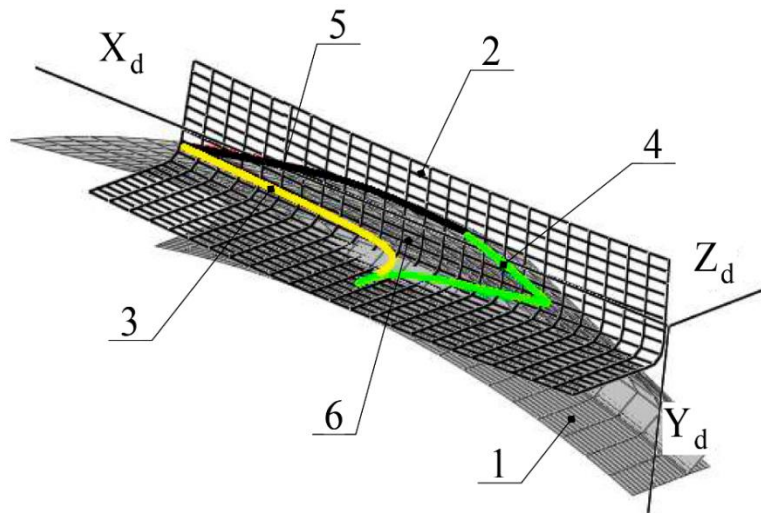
Пляма контакту зуба фрези та оброблюваної поверхні розподільного валу
